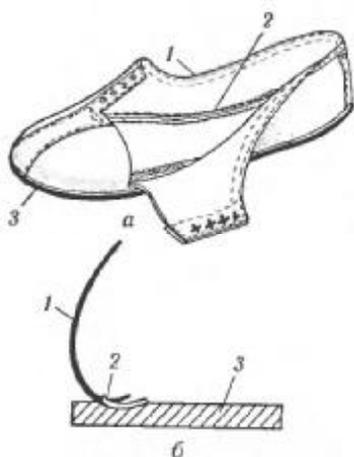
Виворітне кріплення: а — розріз взуття; б — схема кріплення; 1 — заготівка; 2 — нитковий шов; 3 — підшва
